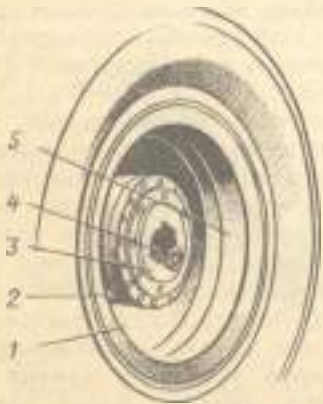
Заправка масла в колесную передачу: 1 — колесный болт; 2 — пробка масляного отверстия; 3 — крышка; 4 — пробка масляного отверстия; 5 — обод колеса
